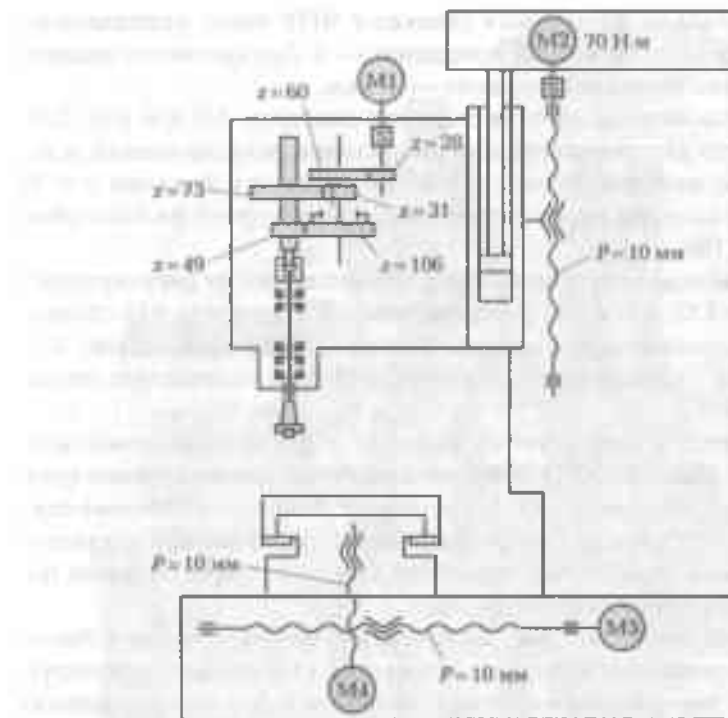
Кинематическая схема фрезерного станка с числовым программным управлением
